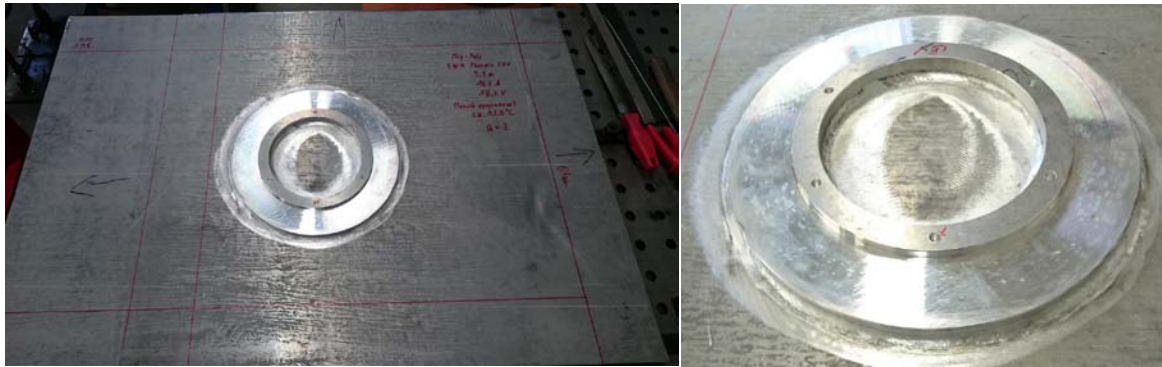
Demonstrator, Grundplatte Arbeitskorb mit befestigtem Ring
